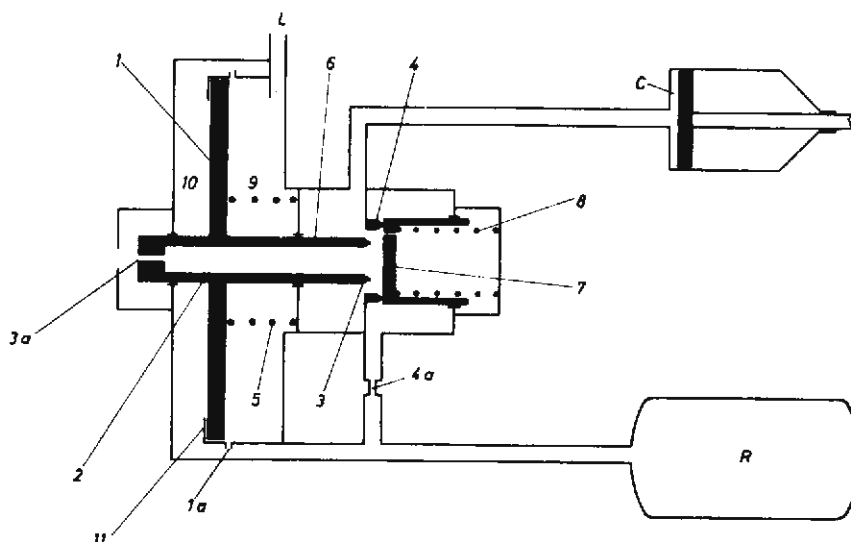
Styreventil, type Fe 115. Ladestilling.
